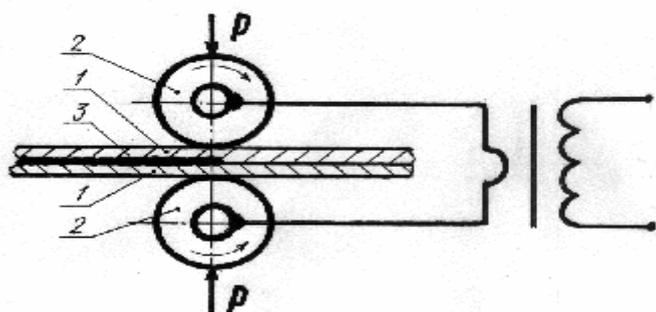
Схема контактной шовной сварки: 1 – заготовка; 2 – электрод-ролик; 3 – сварной шов
